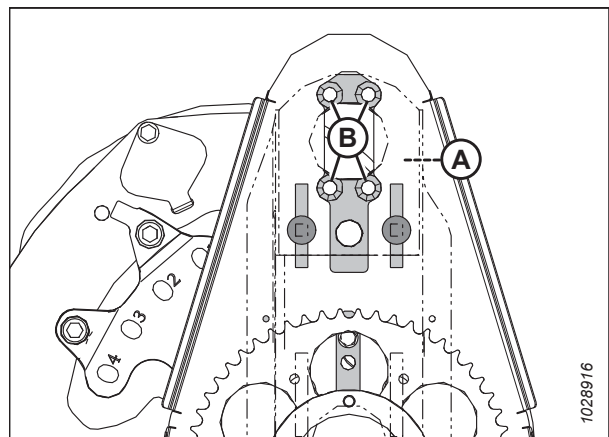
Befestigungsbohrungen des Haspelantriebsmotors
